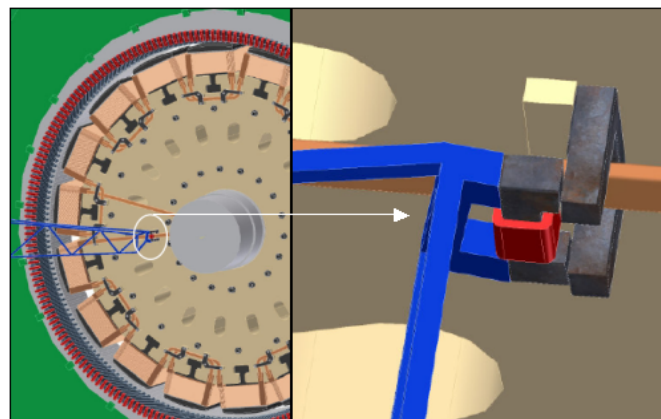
Vista Geral da Montagem do Sistema no Rotor
